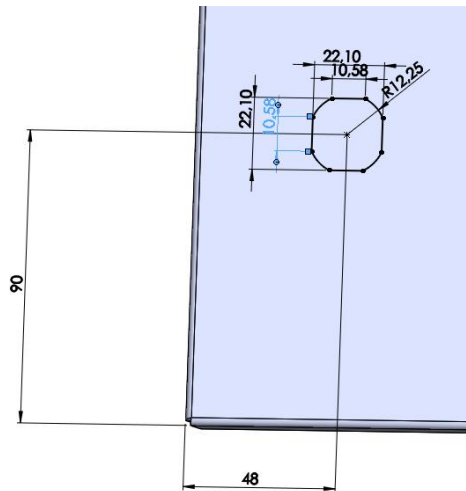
Medidas mecanizado para cierre cuarto de vuelta
